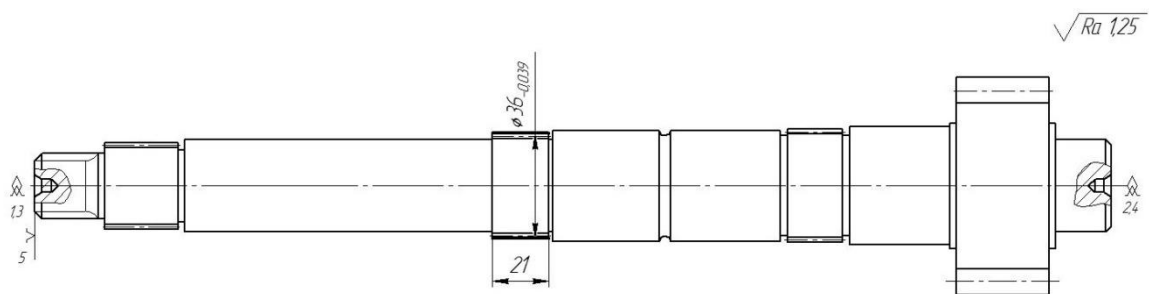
Схема орієнтування вала при шліфуванні зовнішньої поверхні шліцьової частини.
